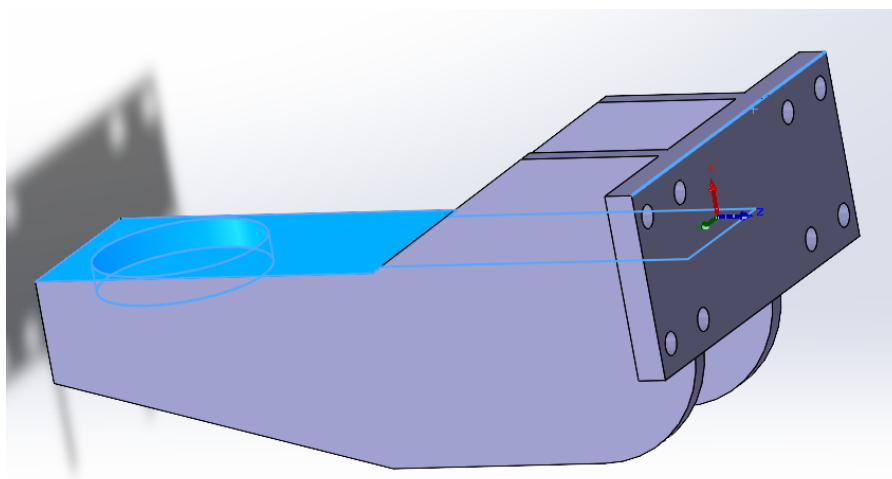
SolidWorks CAM – кронштейн підшипника з визначеною заготовкою (Stock) для САМ-обробки.
